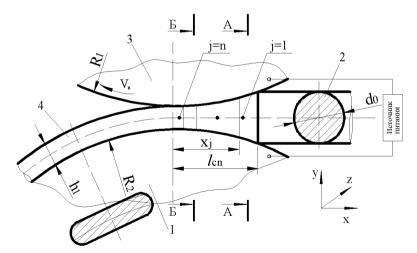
Расчетная схема процесса наплавки цилиндрической детали (1 — наплавляемая деталь; 2 — круглая проволока; 3 — ролик-электрод; 4 — наплавленная поверхность)
